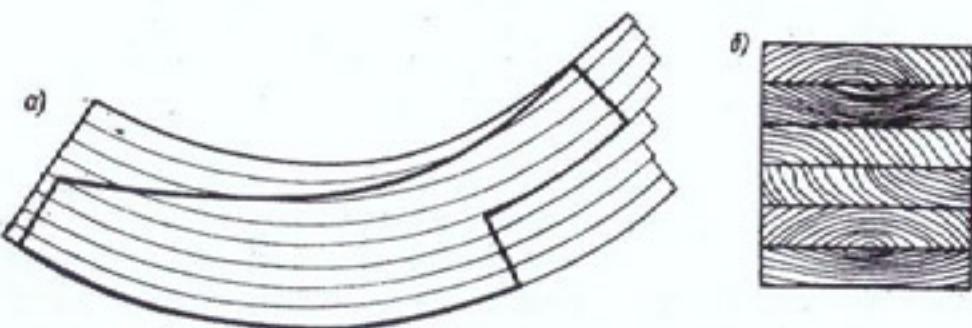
Рекомендуемое укладывание реек в пакет при склеивании: а — заготовки для криволинейной детали; б — с учетом направления волокон (сердцевина к сердцевине, заболонь к заболони).
